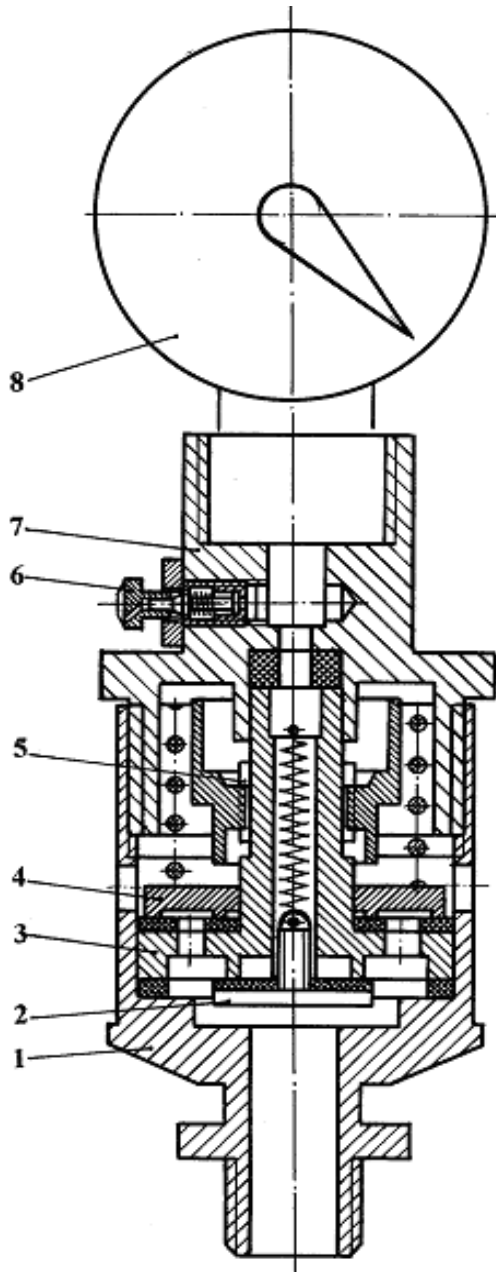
Схема и общий вид диагностического прибора АГЦ-2
